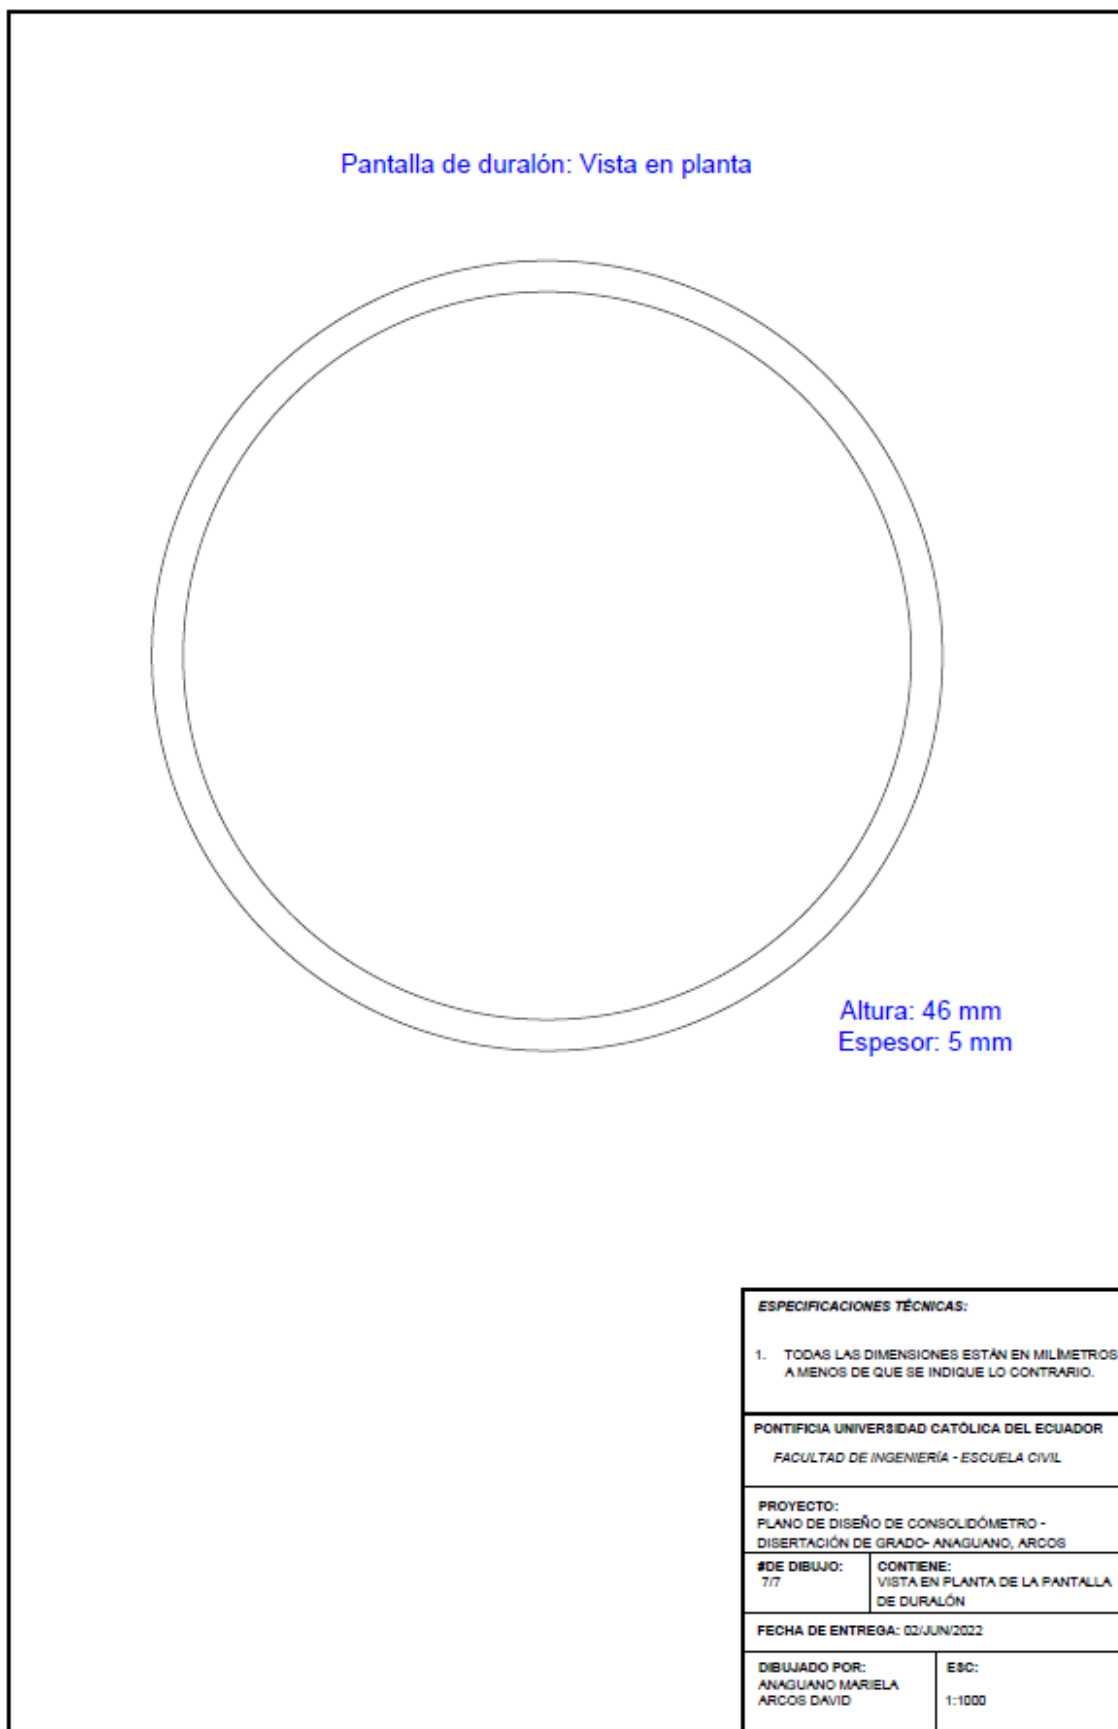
Plano de diseño del consolidómetro. Vista en planta de la pantalla de duralón. Elaboración propia.
